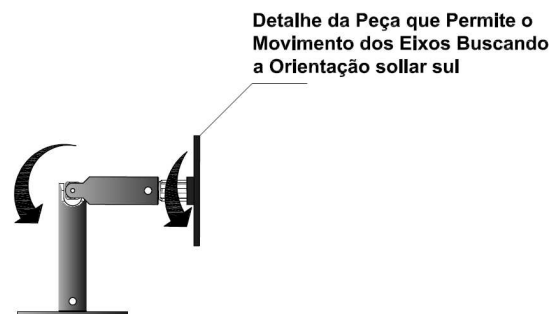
Pormenor da peça que permite a movimentação de rotação e em torno do eixo horizontal.
